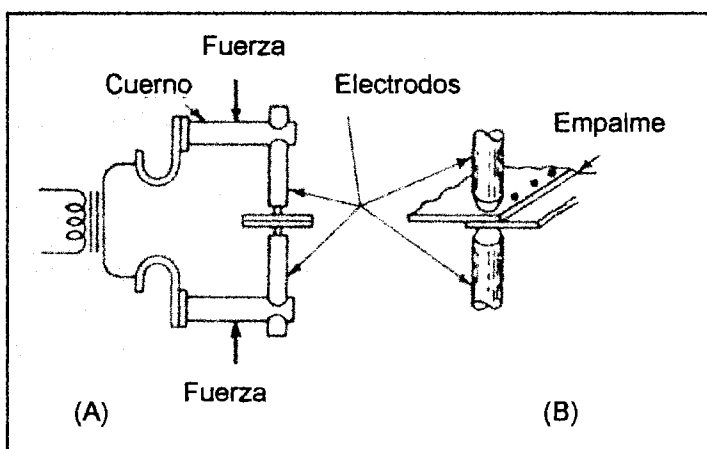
A) un circuito típico de soldadura de puntos. B) un empalme soldado con puntos.
